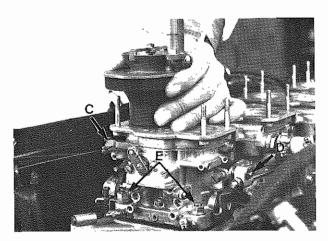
C - Morsetto cavo starter Starter cable clamp
